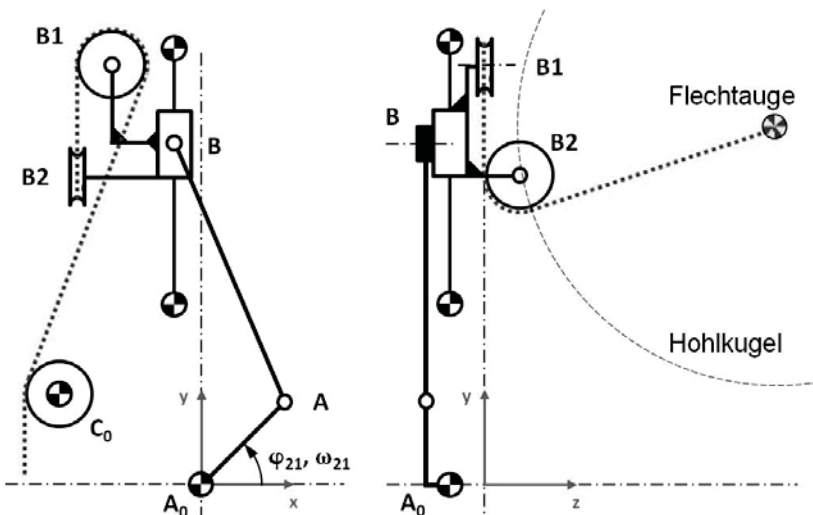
Berechnungsskizzen des Verlegemechanismus: Draufsicht (links) und Seitenansicht (rechts)
